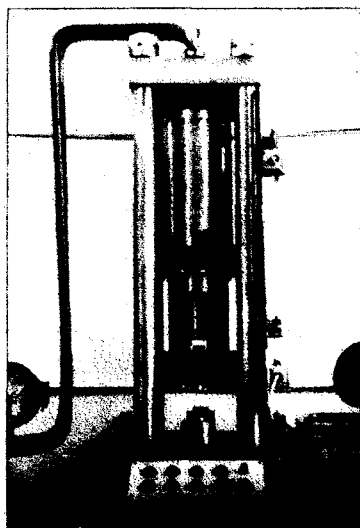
Верхняя часть пресса для выдавливания с активными силами трения
